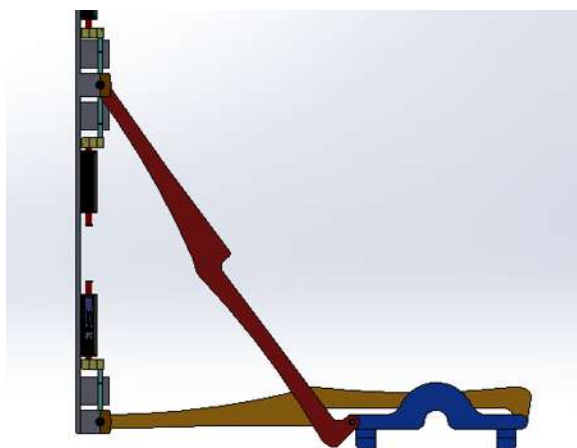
Forma Final del mecanismo de Chebyshev
